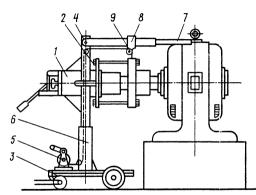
Приспособление для извлечения ротора из статора электродвигателя:
